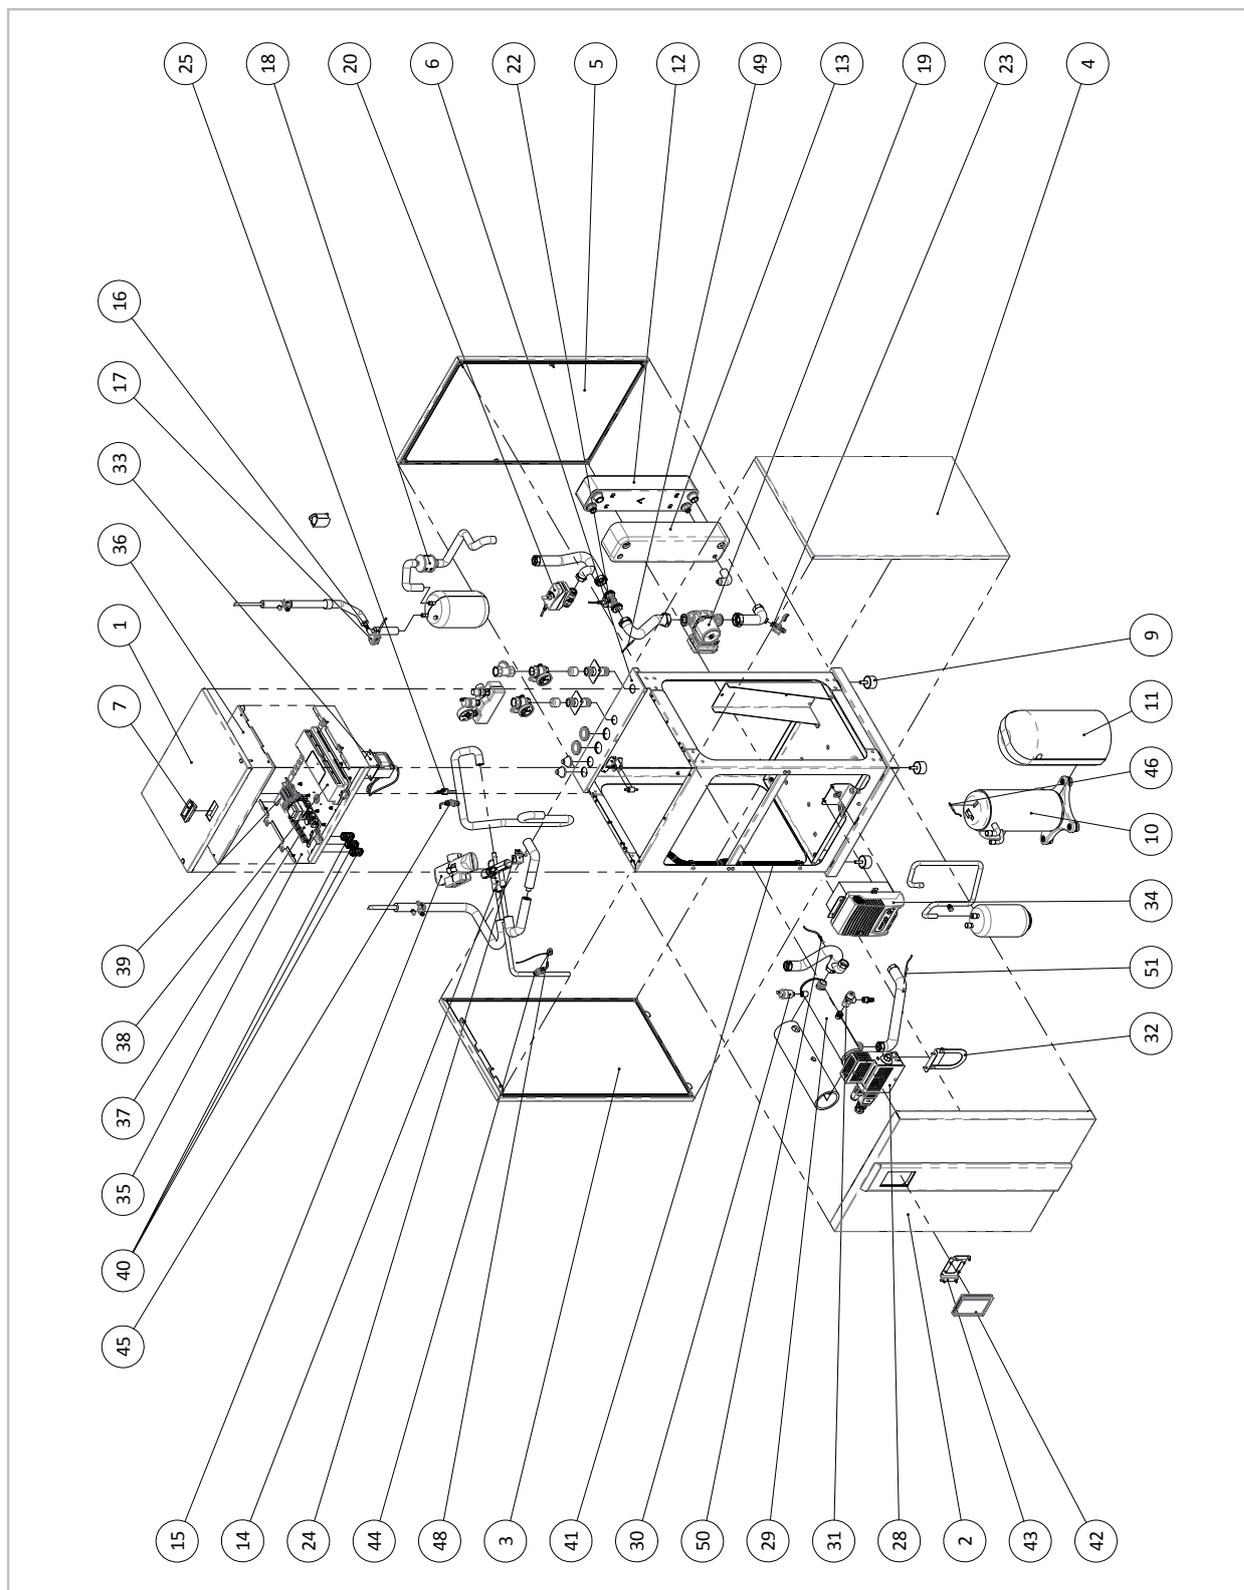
Vue éclatée du module interne HTS 80/90/110/130/200/260
